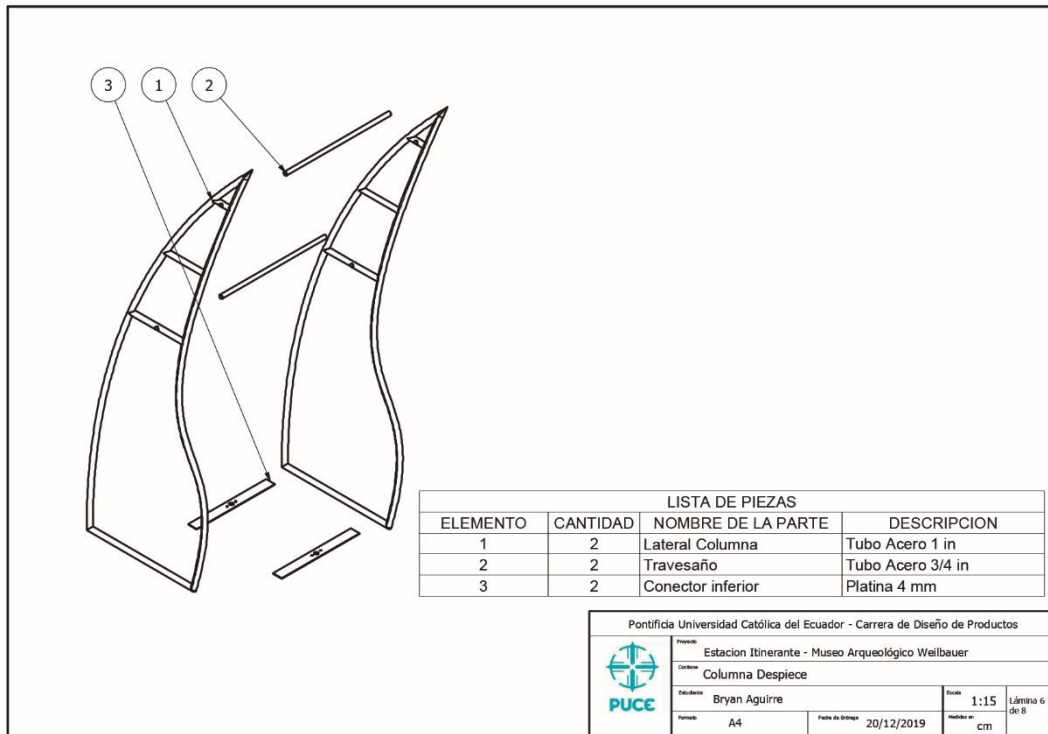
Detalle de despiece: componentes de las Columnas. Fuente elaboración propia.
